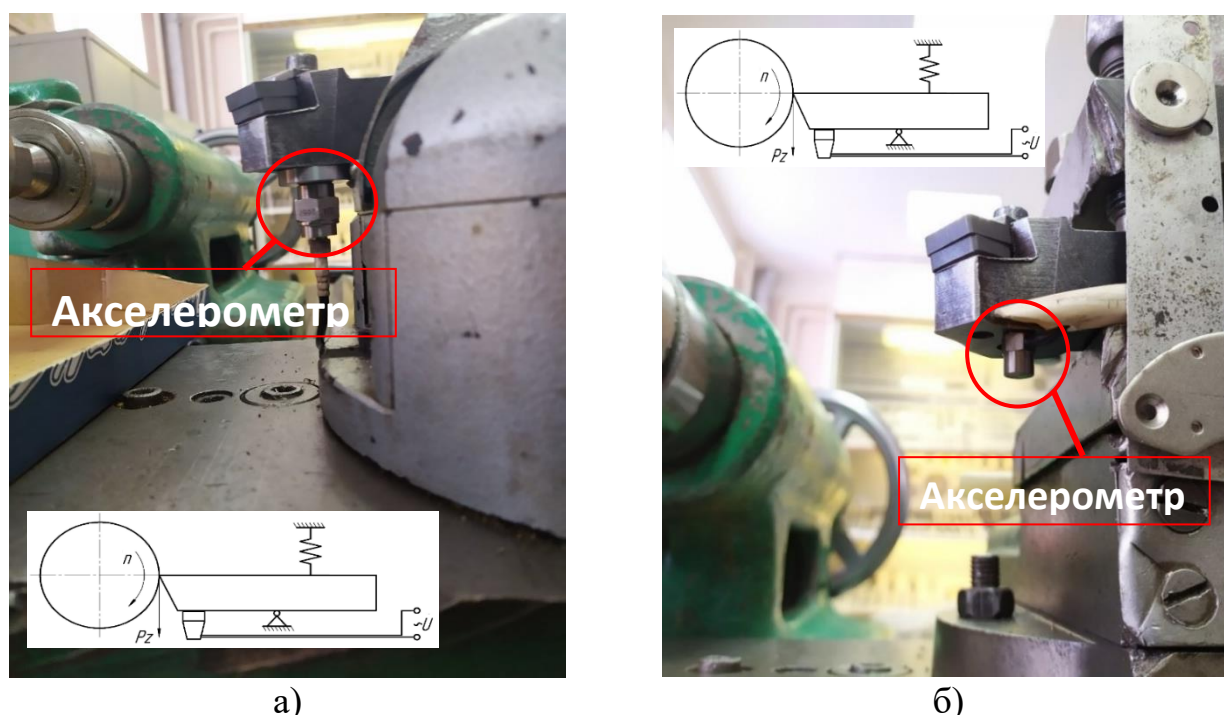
Расположение: а – активного вибродатчика на державке сборного резца в динамометре УДМ600; б – расположение генераторного датчика на державке сборного резца в штатном резцедержателе
